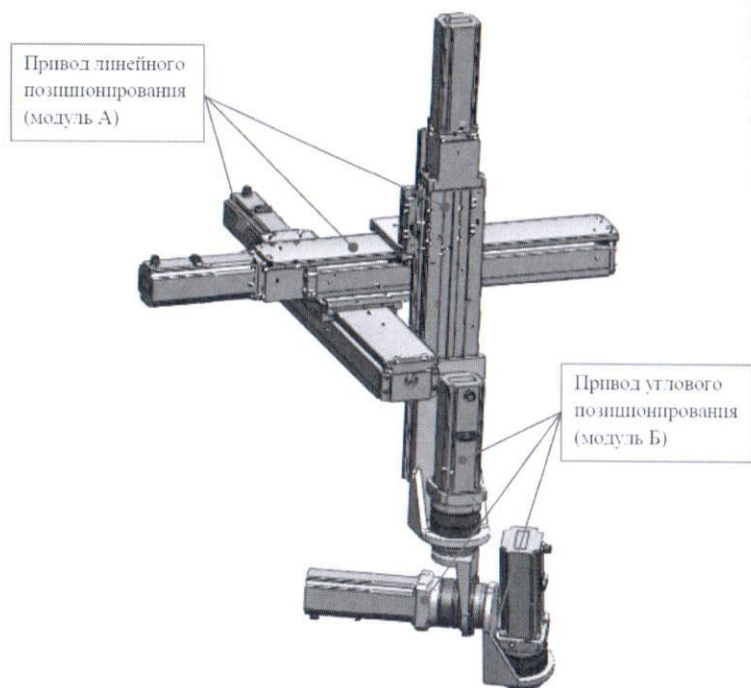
Лабораторный 6-координатный автоматизированный манипулятор
